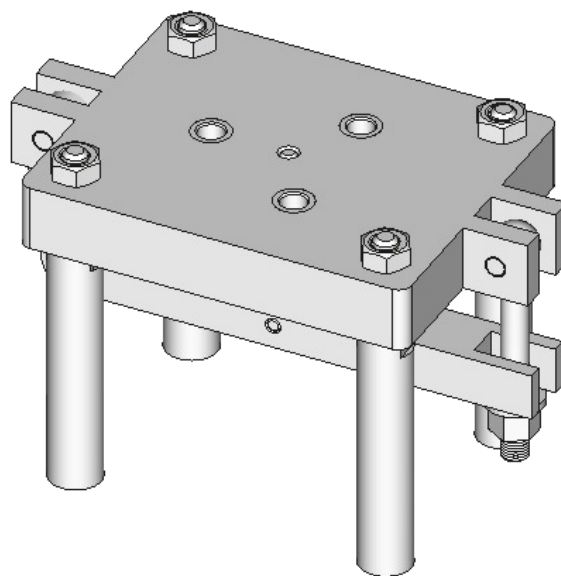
Кондуктор с прихватом рычажного типа
